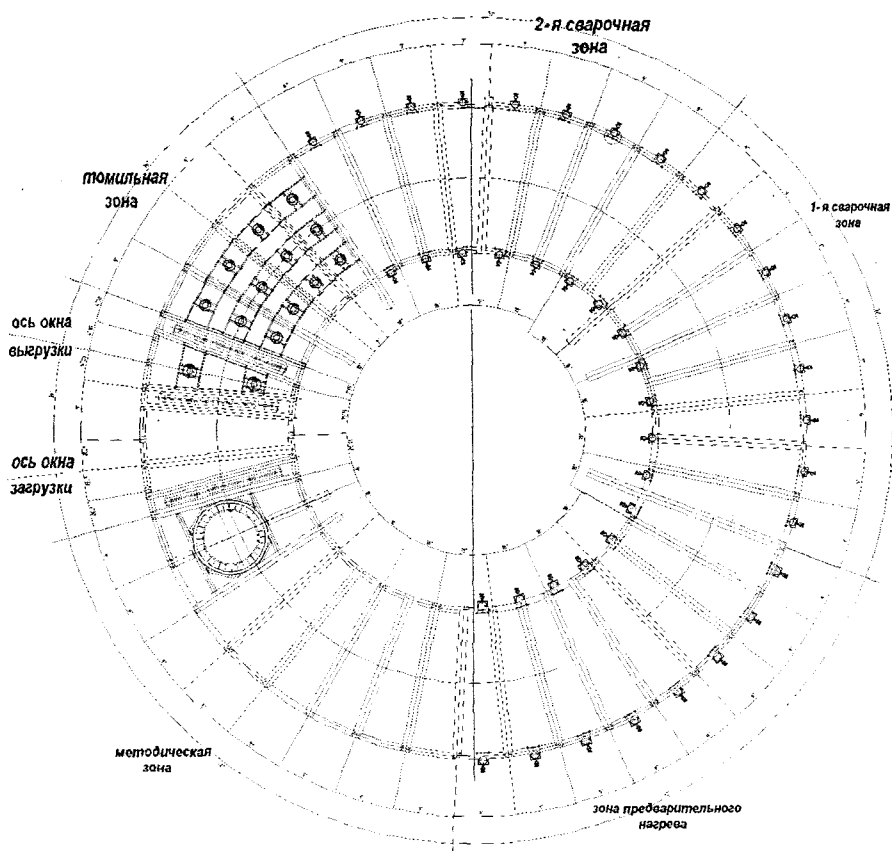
Схема кольцевой печи для нагрева трубных заготовок РУП «БМЗ»
